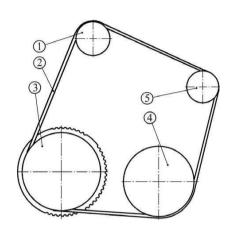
Схема установки ремня привода вспомогательных агрегатов:
